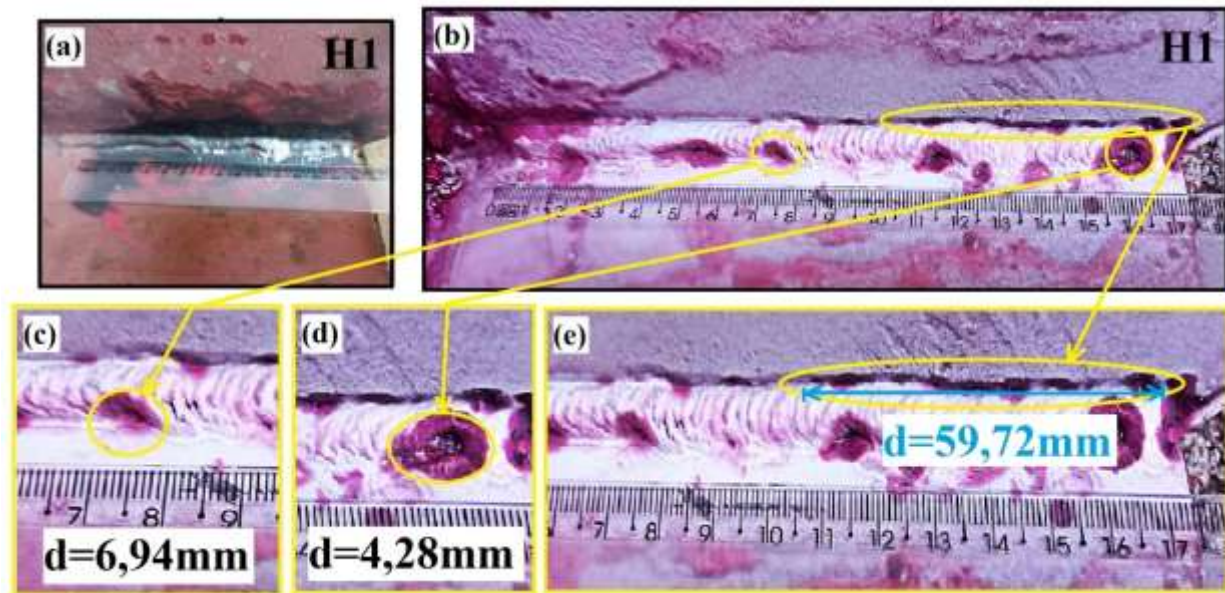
Inspeção por líquido penetrante e análise: coluna “X”, cordão de solda H1.
